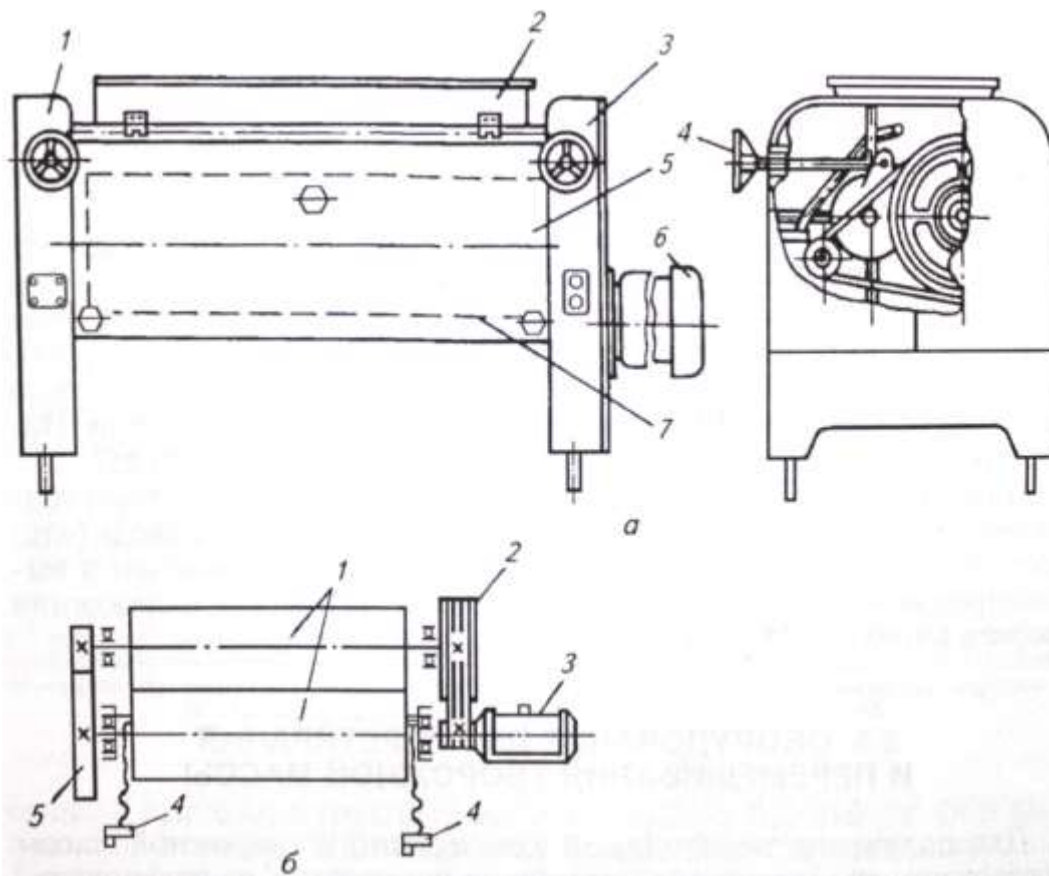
Вальцовка для творога Е8-ОПУ:
